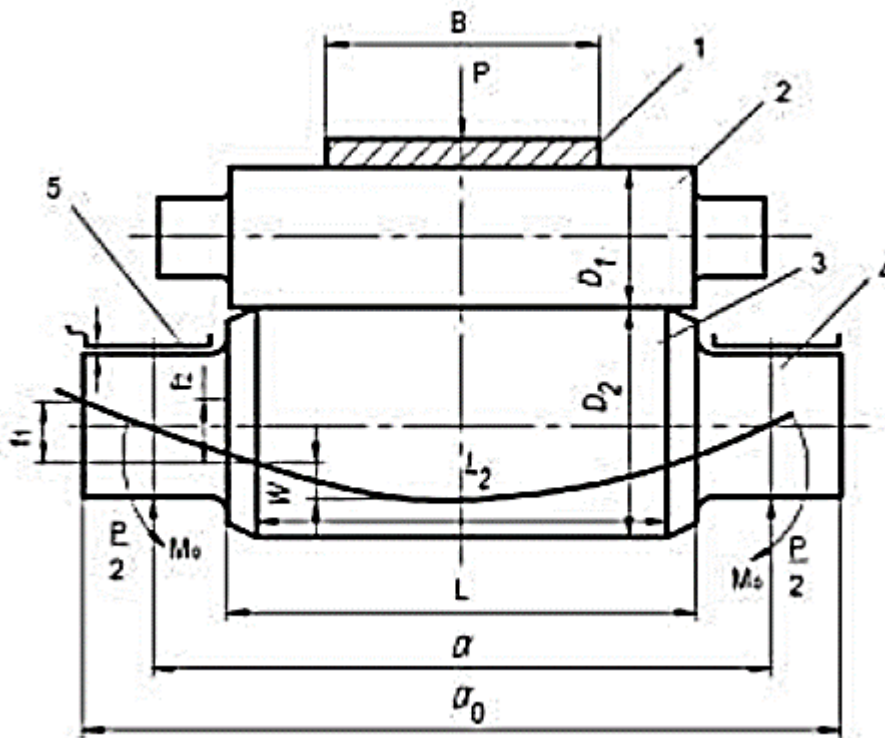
Валковий вузол чотирьохвалкову кліт: 1 штаба; 2 – робочий валок; 3 - опорний валок; 4 - шийка опорного валка; 5 – підшипник кочення
